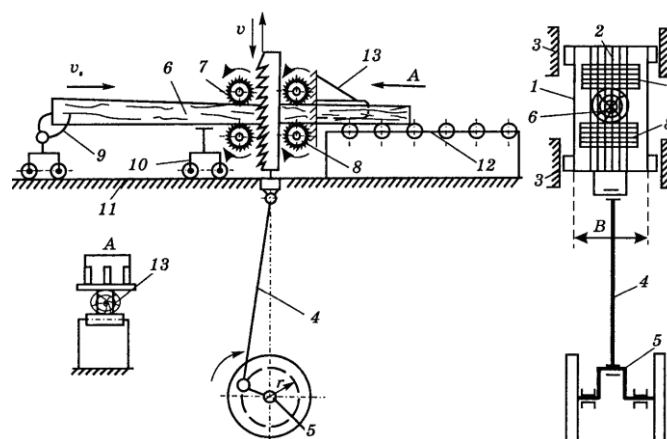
Принципова схема двоповерхової вертикальної пилорами: 1 — пилкова рамка; 2 — пилки; 3 — напрямні; 4 — шатун; 5 — кривошипний вал; 6 — колода; 7, 8 — подавальні вальці; 9, 10 — передрамні візки; 11 — рейковий шлях; 12 — роликовий стіл; 13 — напрямний апарат
